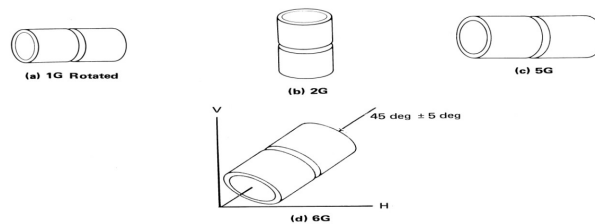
POSICIONES DE TUBOS PARA SOLDADURA DE CANAL.
